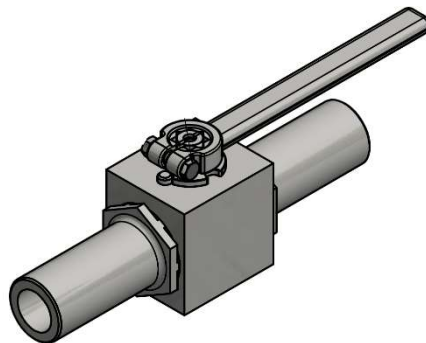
Zusammengebaute Kugelhahnlösung C mit Schweißanschlussvariante
